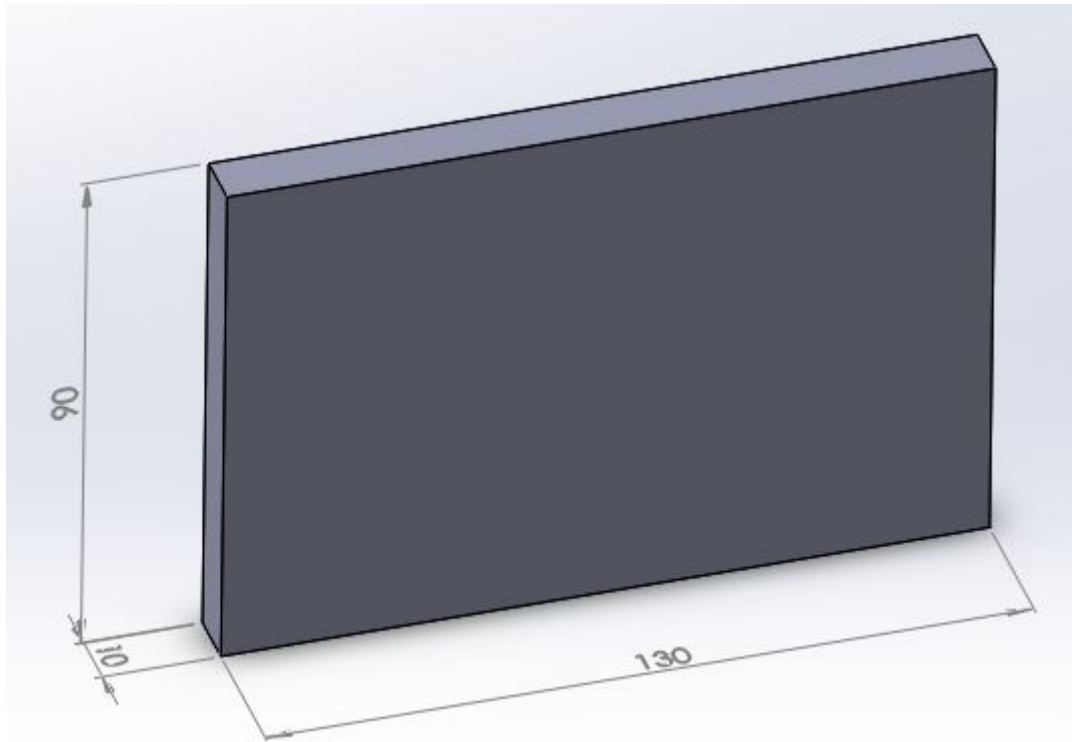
Fabricación. Plantilla de aluminio 7075-T6.
